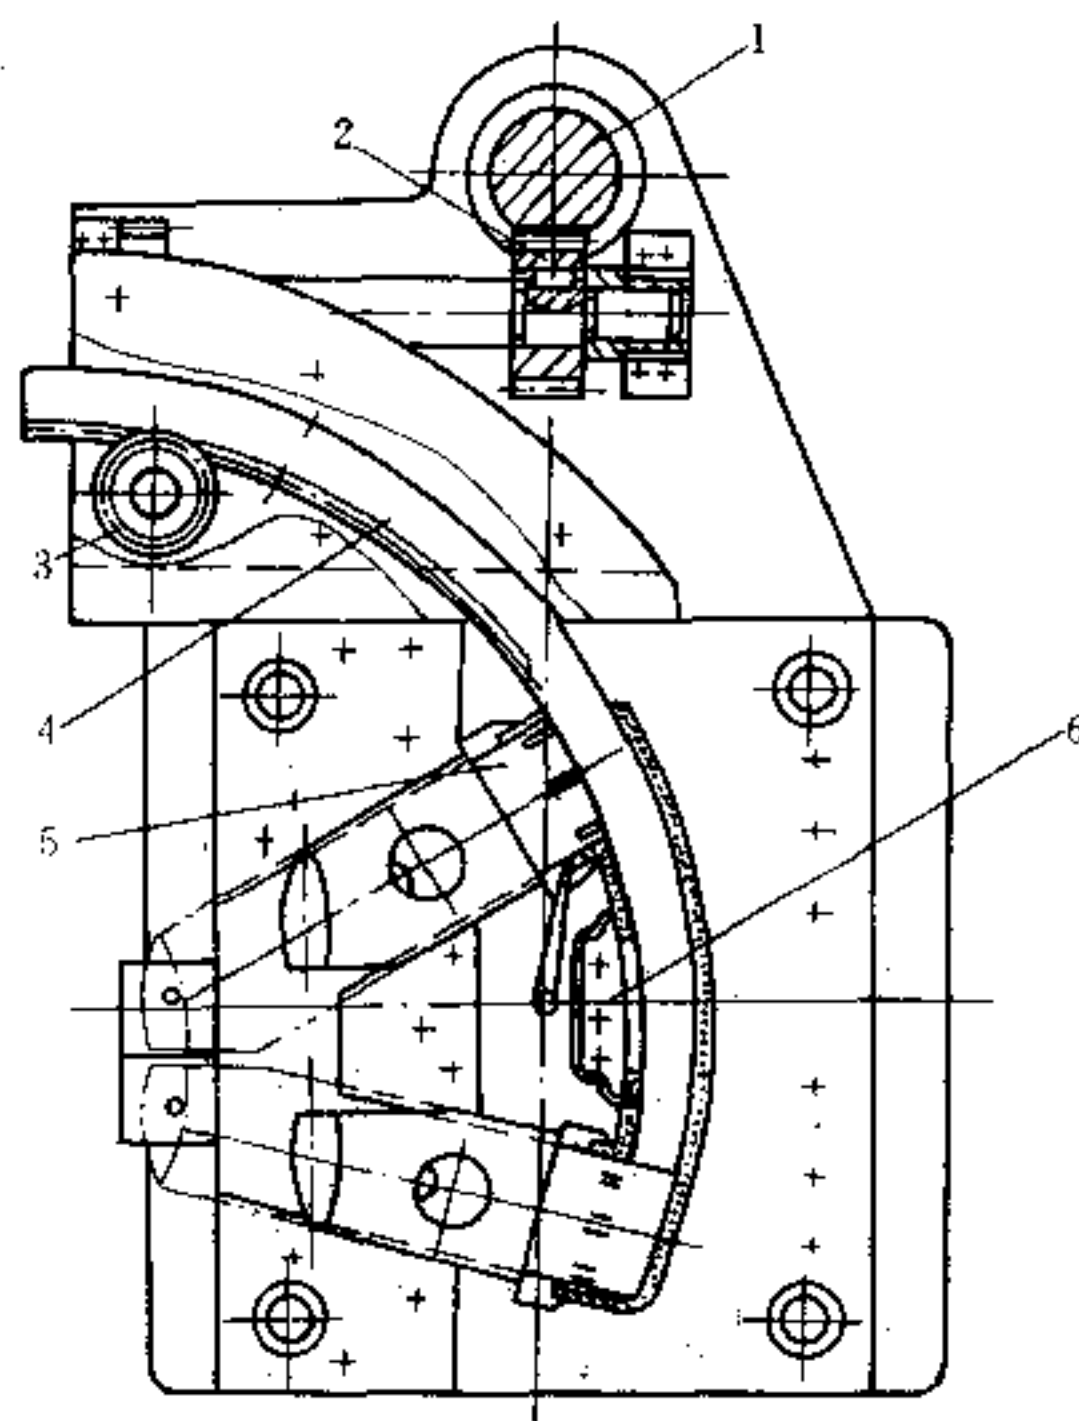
内齿轮传动的弯型芯圆弧抽芯机构
